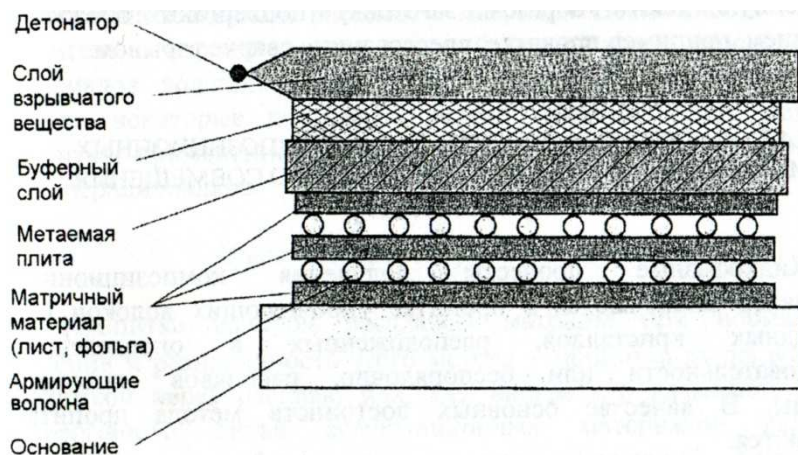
Получение МКМ методом сварки взрывом
